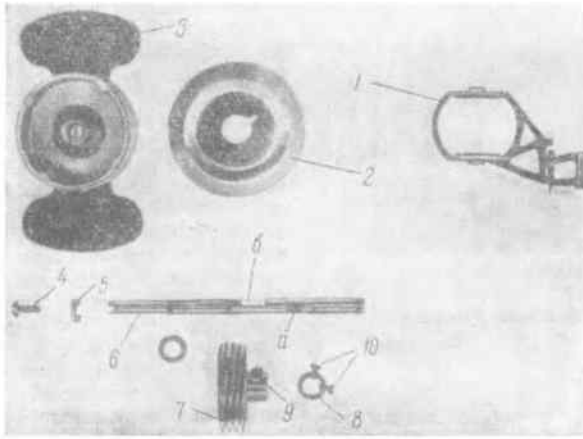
Главный вал головки кинопроектора (крепящиеся на нем детали сняты)
